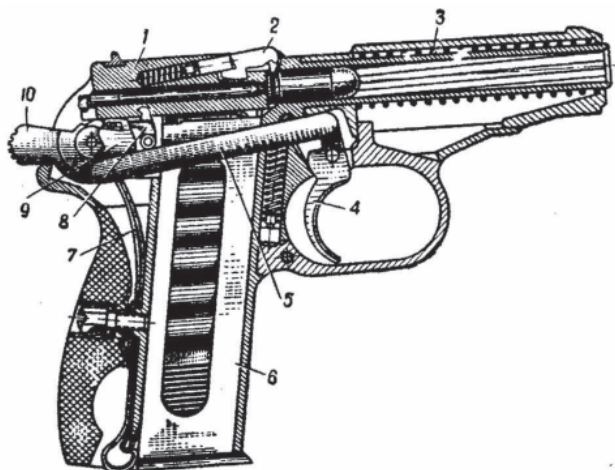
Положение частей и механизмов пистолета перед выстрелом: 1 – затвор; 2 – выбрасыватель; 3 – возвратная пружина; 4 – спусковой крючок; 5 – спусковая тяга; 6 – магазин; 7 – боевая пружина; 8 – шептало с пружиной; 9 – рычаг взвода; 10 – курок
